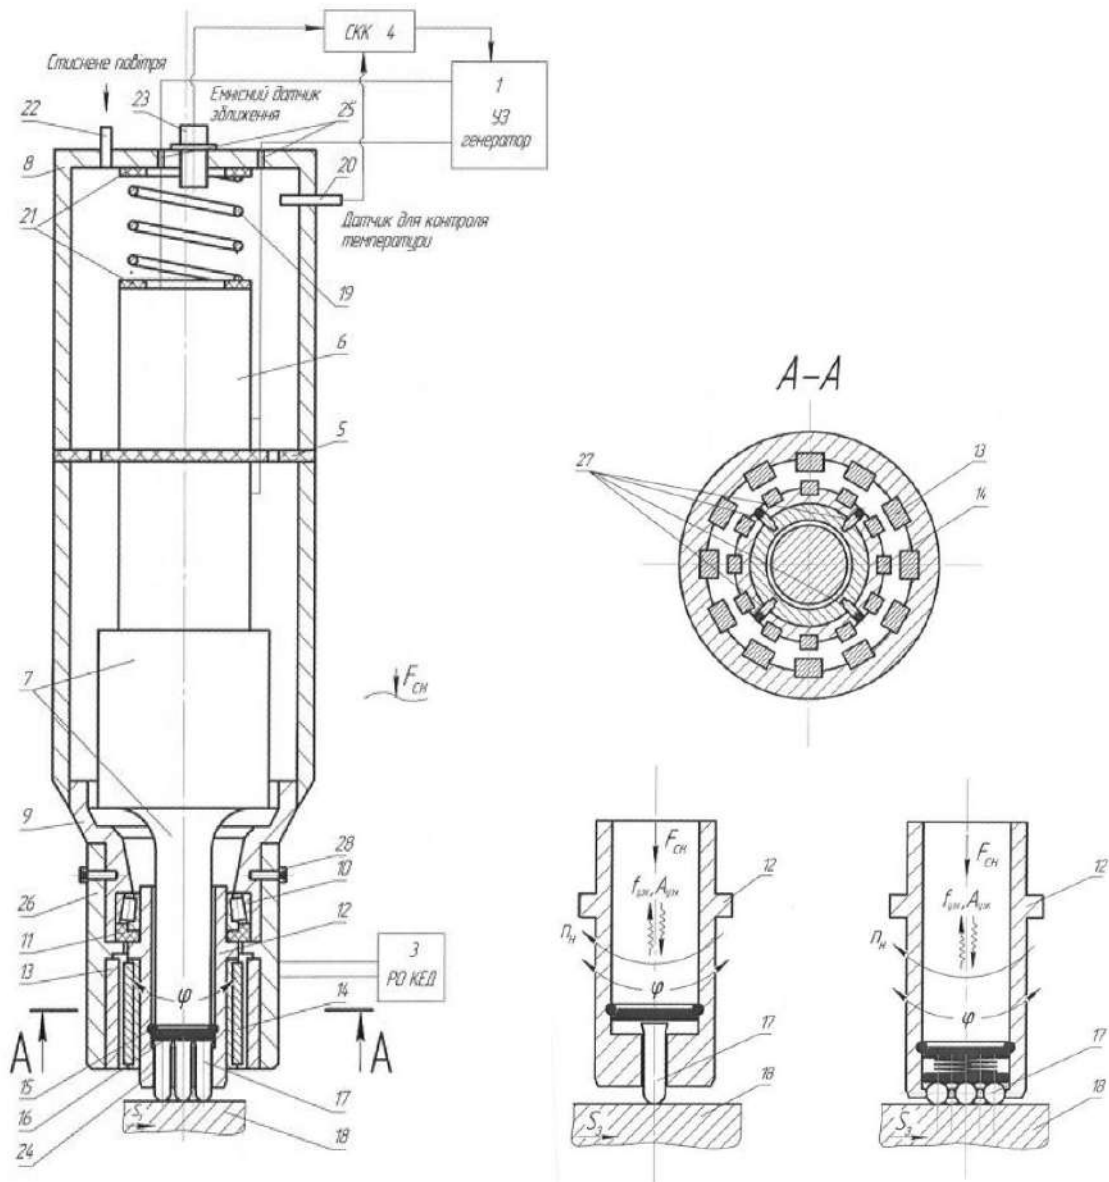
Конструкція установки для поверхневої оздоблювально-зміцнювальної обробки
